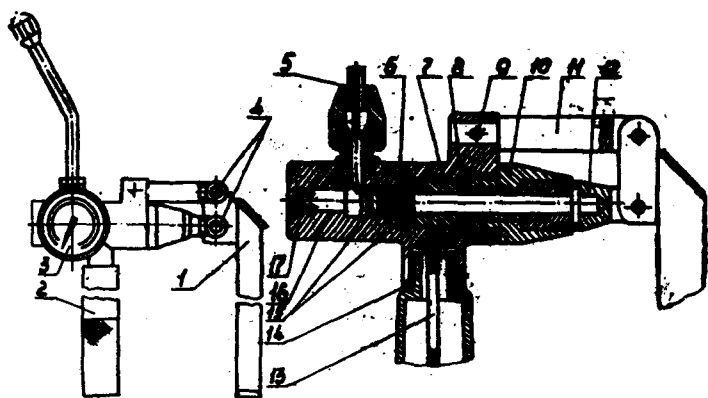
Приспособление для проверки форсунок и прецизионных пар топливного насоса
